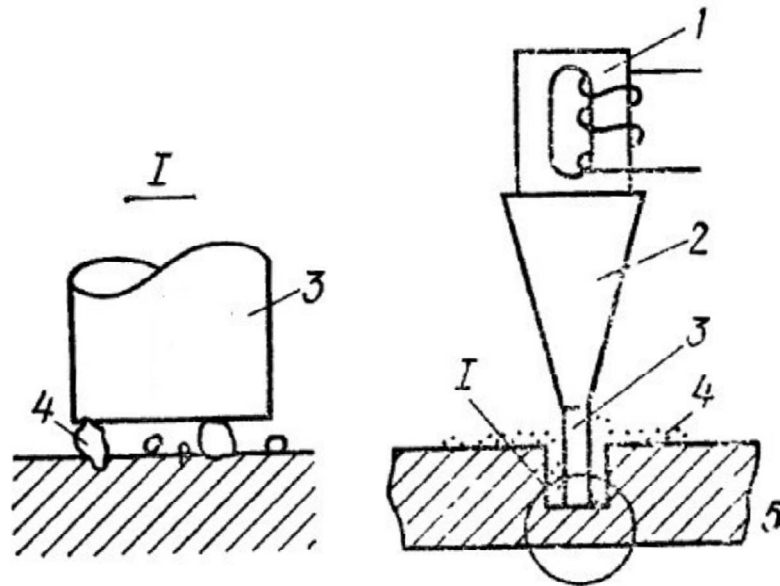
Механізм ультразвукової розмірної обробки:
